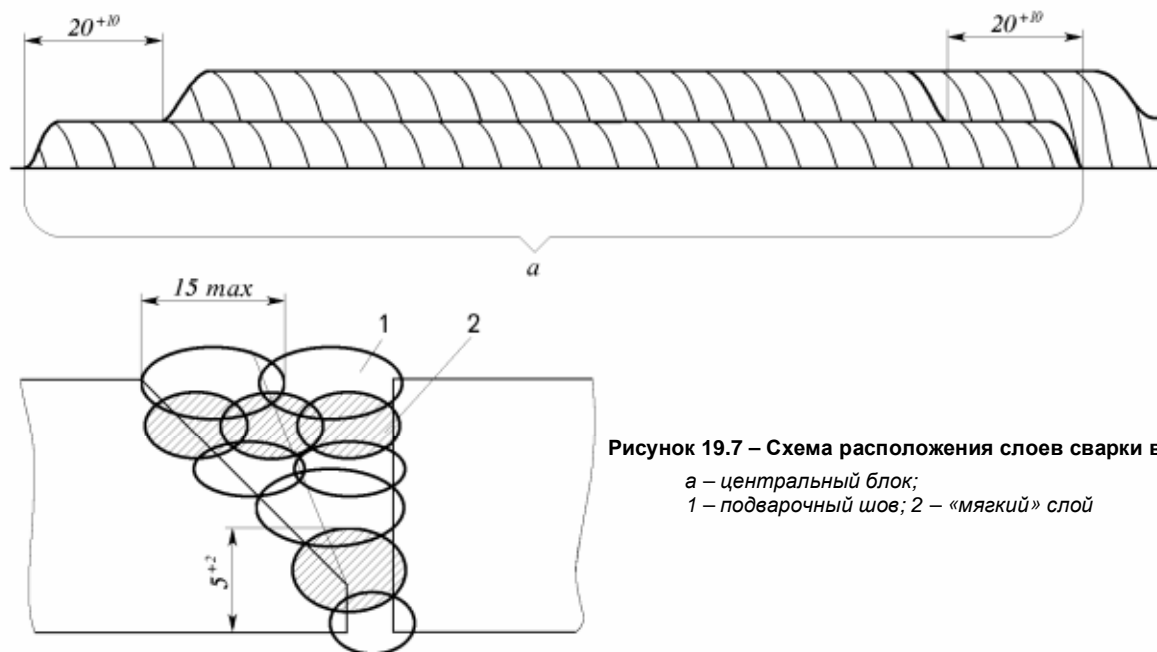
Схема расположения слоев сварки в блоке:
